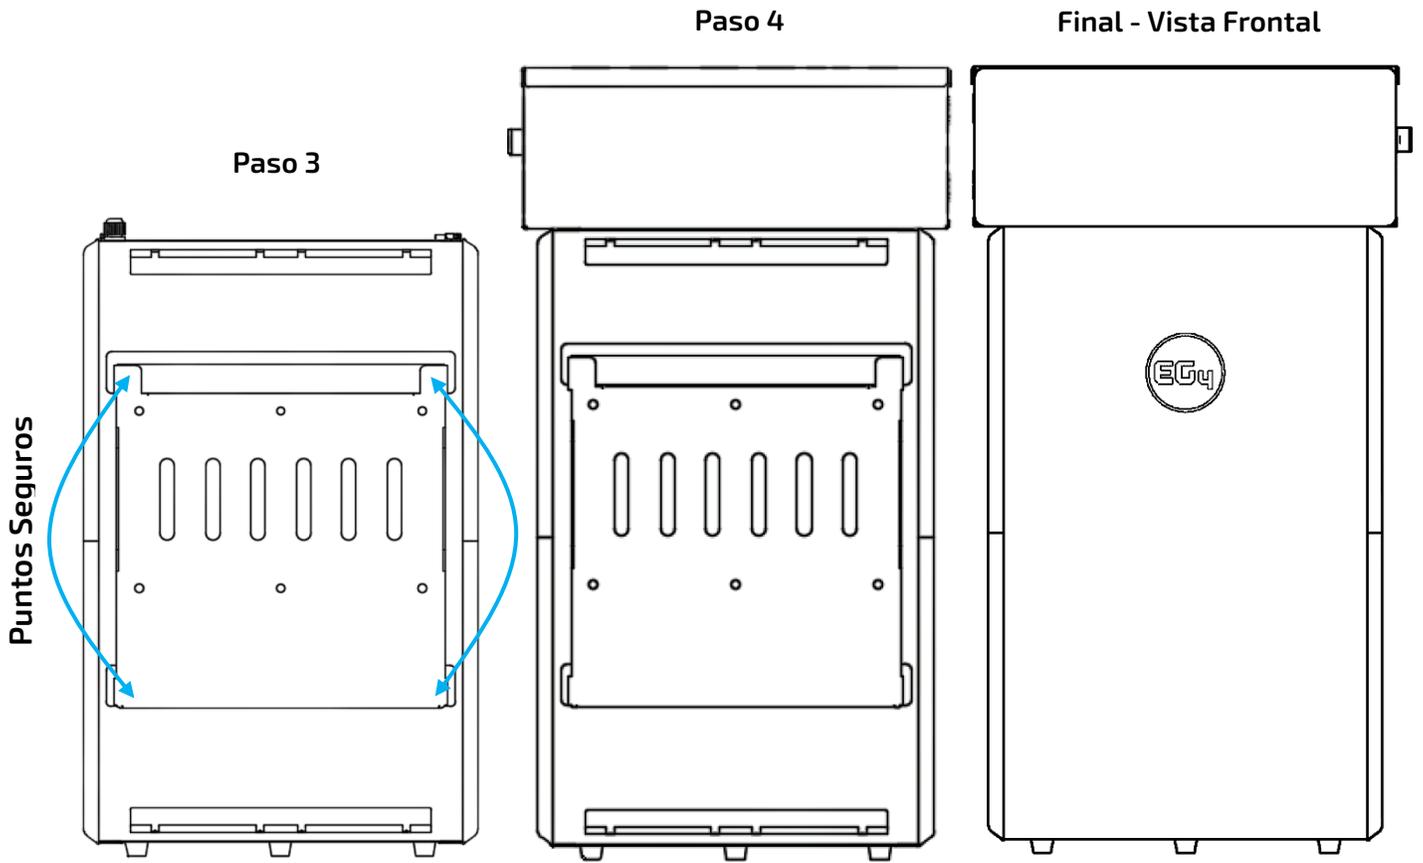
WallMount Instalación Con Caja de Conducto Pasos 3, 4 y 5
